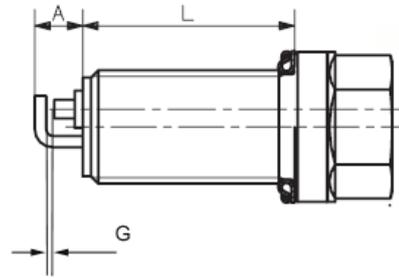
Dimensionen der Zündkerze Typ 6118A...
